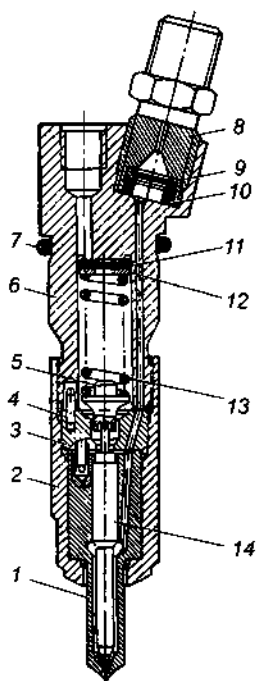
Форсунка: 1 — корпус распылителя; 2 — гайка распылителя; 3 — проставка; 4 — установочный штифт; 5 — штанга; 6 — корпус форсунки; 7 — уплотнительное кольцо; 8 — штуцер; 9 — фильтр; 10 — уплотнительная втулка; 11, 12 — регулировочные шайбы; 13 — пружина; 14 — игла распылителя
